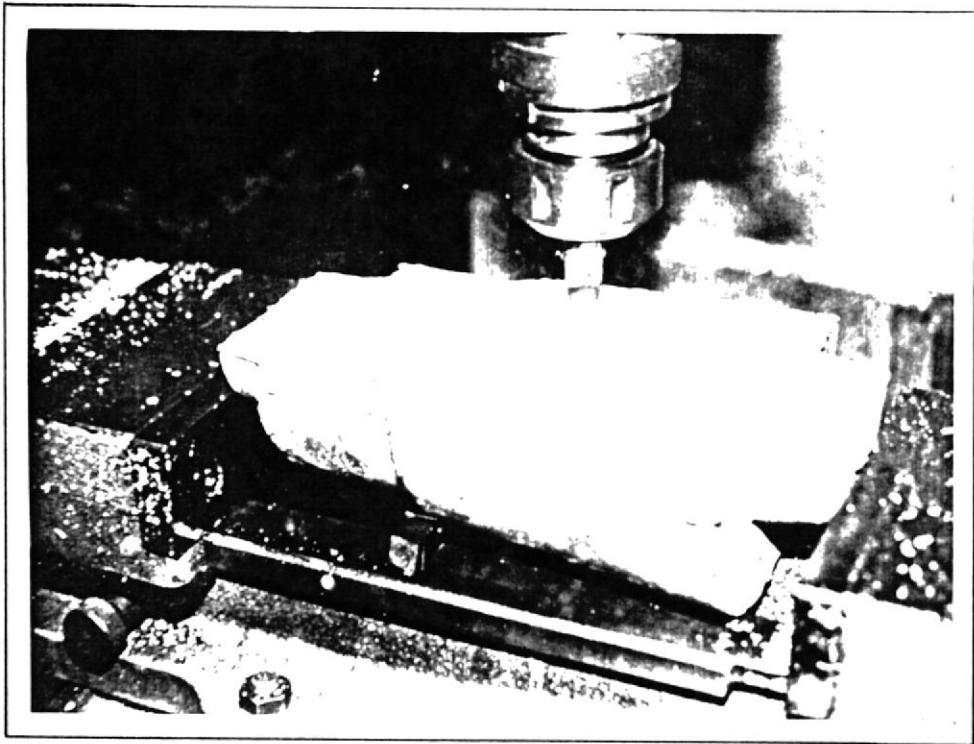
Rectificado de ambas mitades para facilitar ensamblaje.
